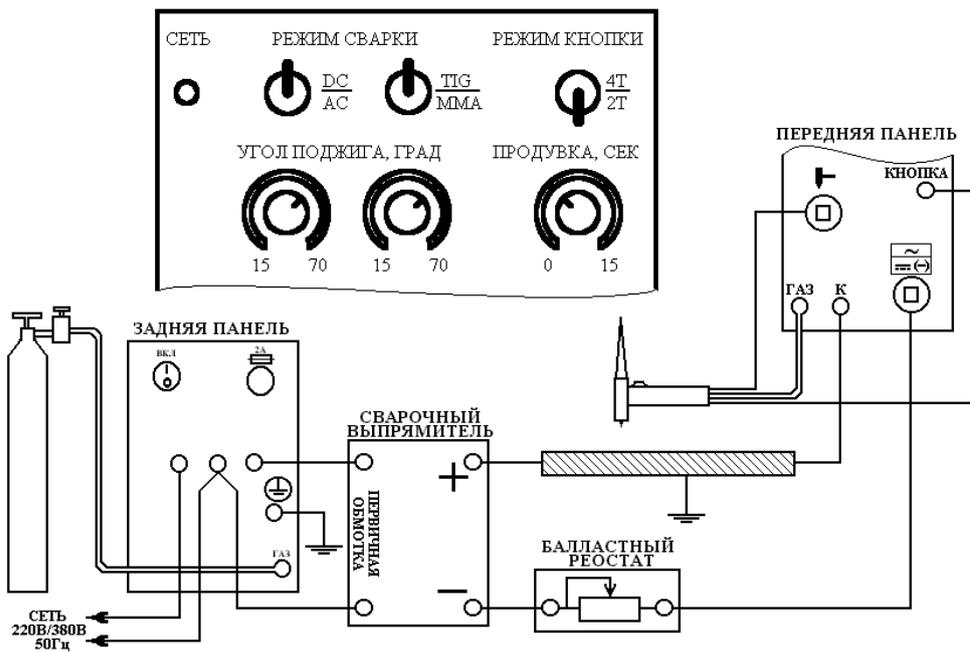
Схема рабочего места для сварки на постоянном токе в режиме TIG
